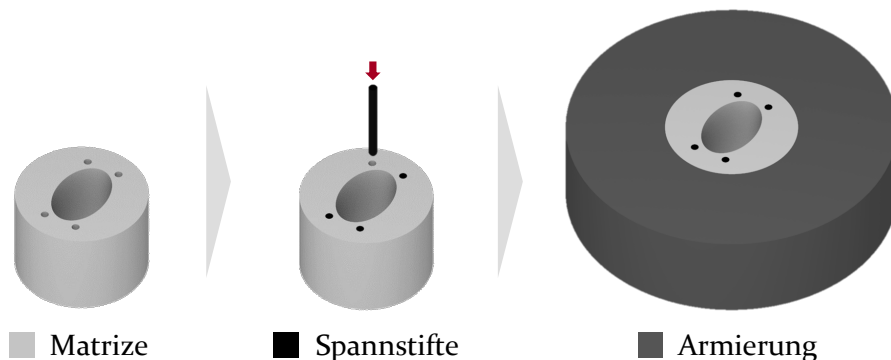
Werkzeugmontage bei Einsatz von Spannstiften
